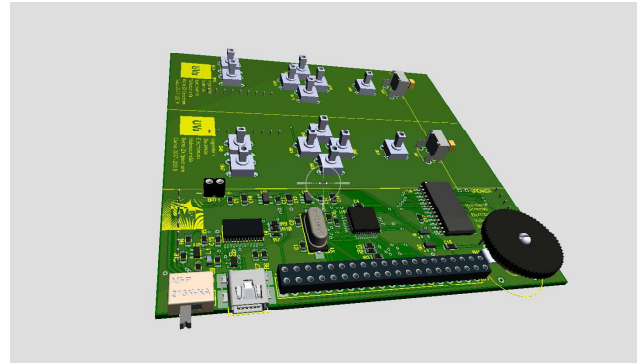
Vista 3D del diseño de la PCB en la versión 1.0.
